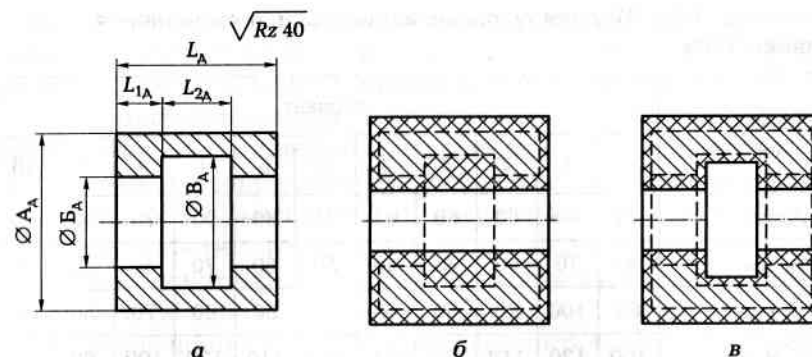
Деталь (а) и варианты (б и в) заготовки для детали
